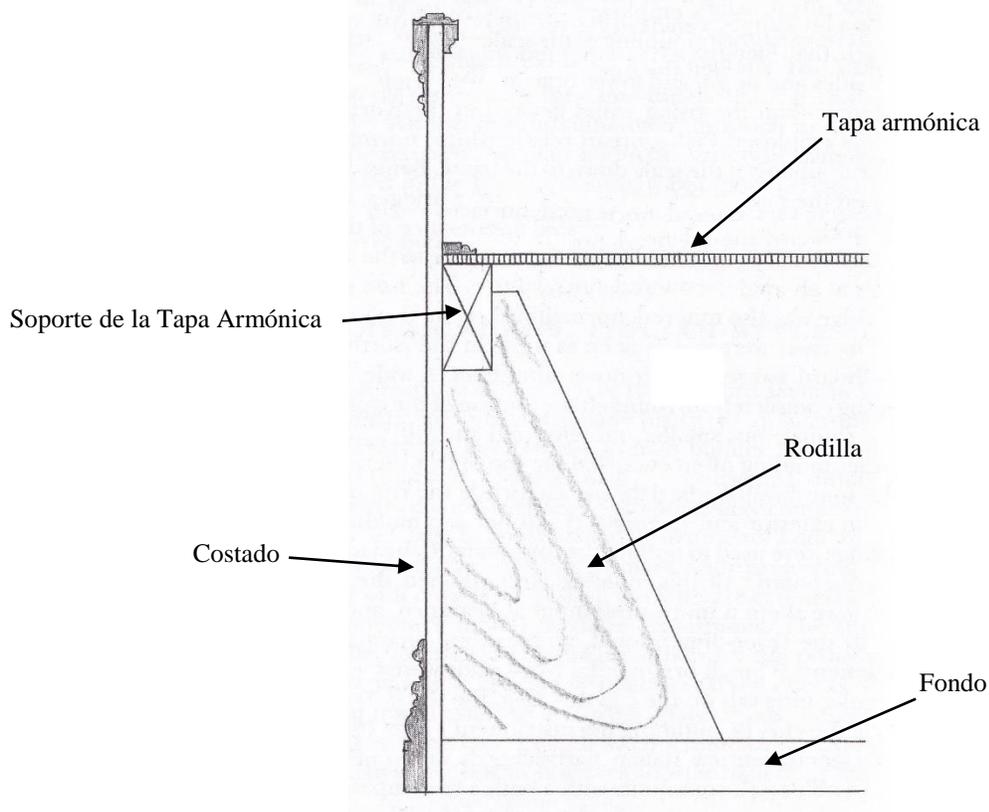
Detalle de la sección transversal típica en un clavecín italiano. Kottick 2003, p. 72.
